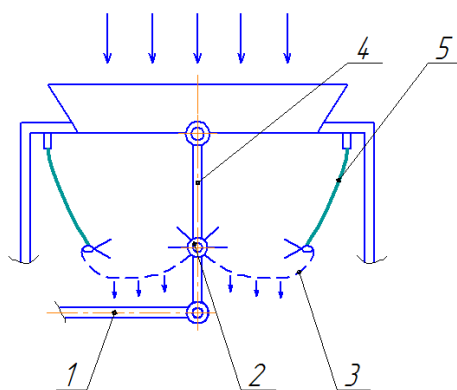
Схема рабочего оборудования цепного агрегата: 1 – шатун; 2 – толкающая штанга; 3 – цепное полотно; 4 – маятниковый рычаг; 5 – эластичные стенки
